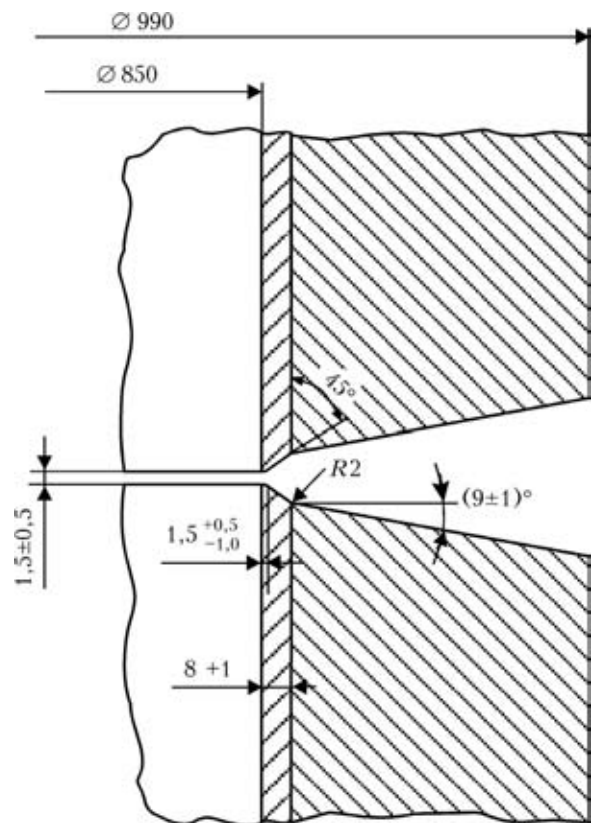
Схема разделки кромок для односторонней сварки трубного соединения из плакированной низколегированной стали
